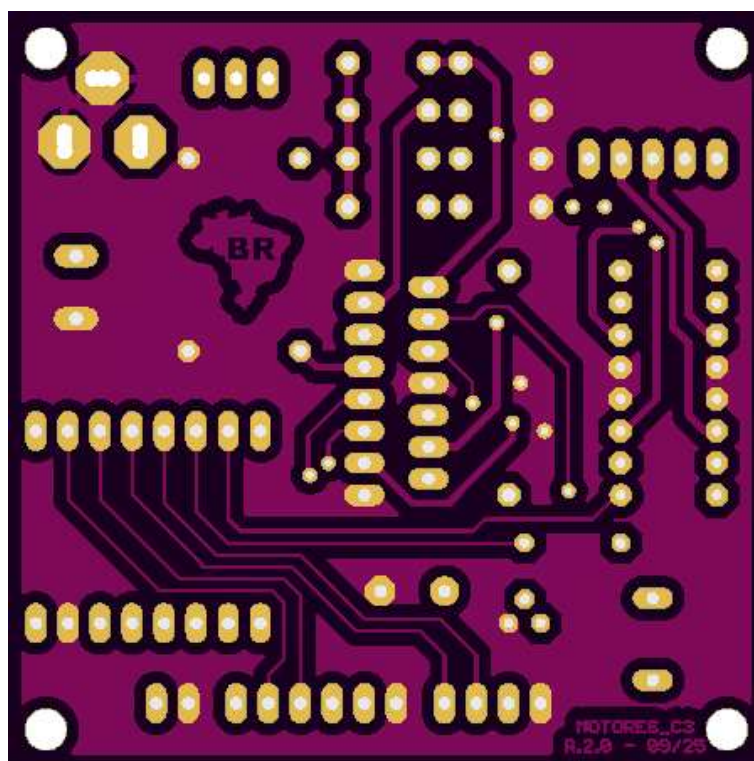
Placa MOTORES_C3 rev. 2.1 (lado da solda)
